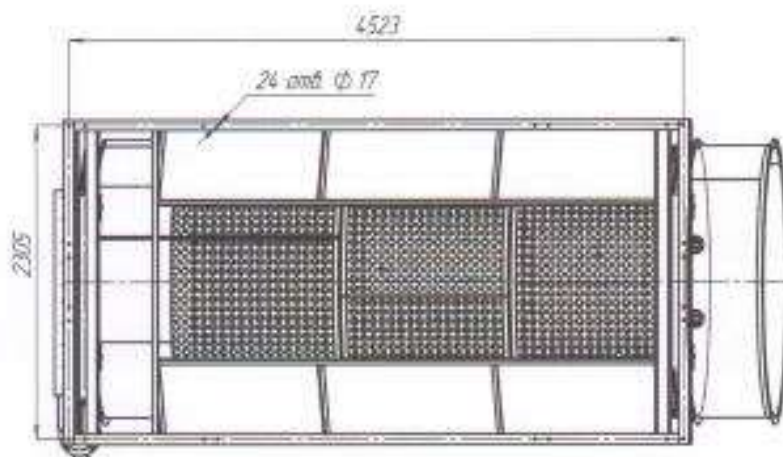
Отверстия для крепления сепаратора к опорной конструкции.
